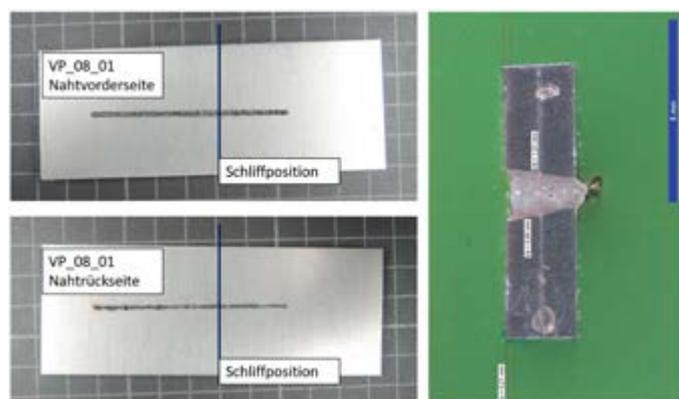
Fotos einer Probe (links) und Schlibbild einer Schweißnaht (rechts)
